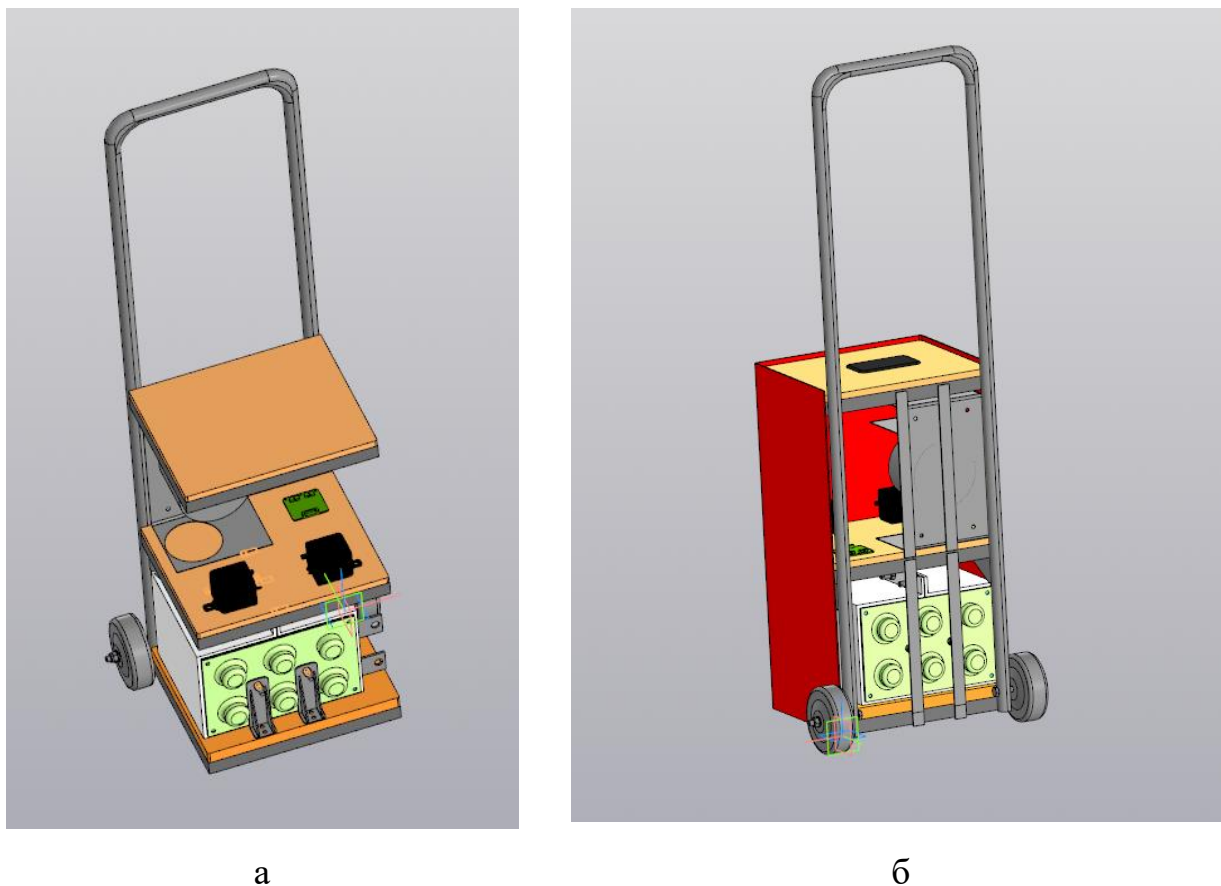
Модель пуско-зарядного устройства в сборе: а – вид спереди, б – вид сзади
